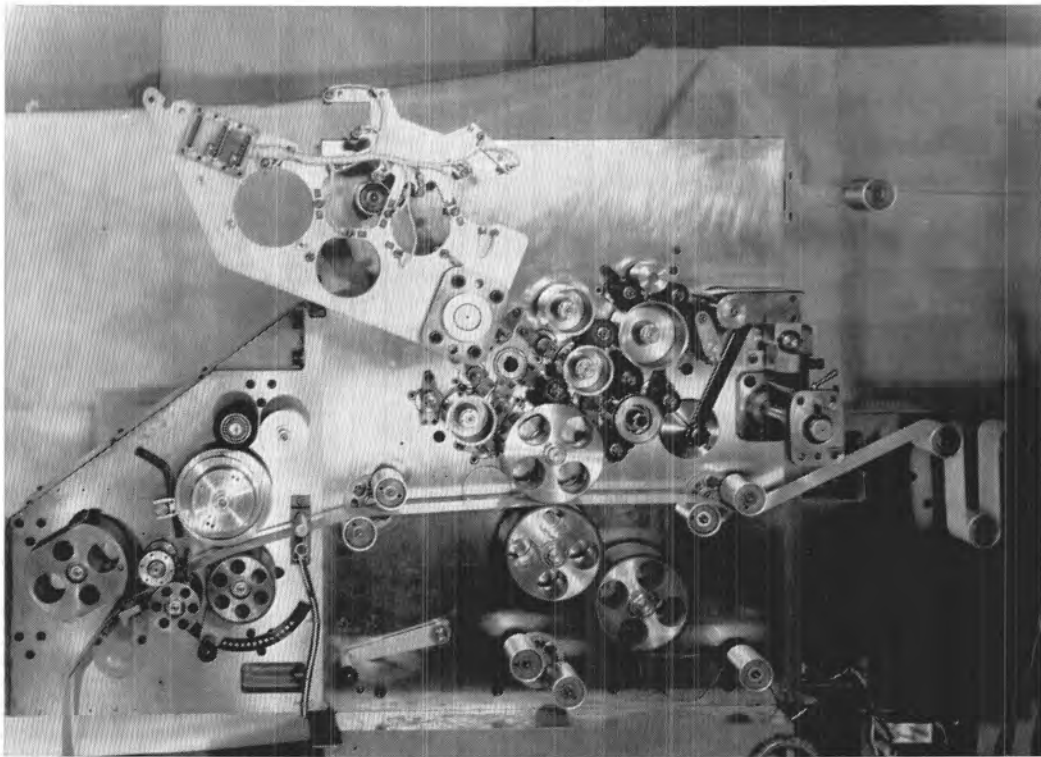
Druckwerk mit abgeschwenkter Hilfswand.
